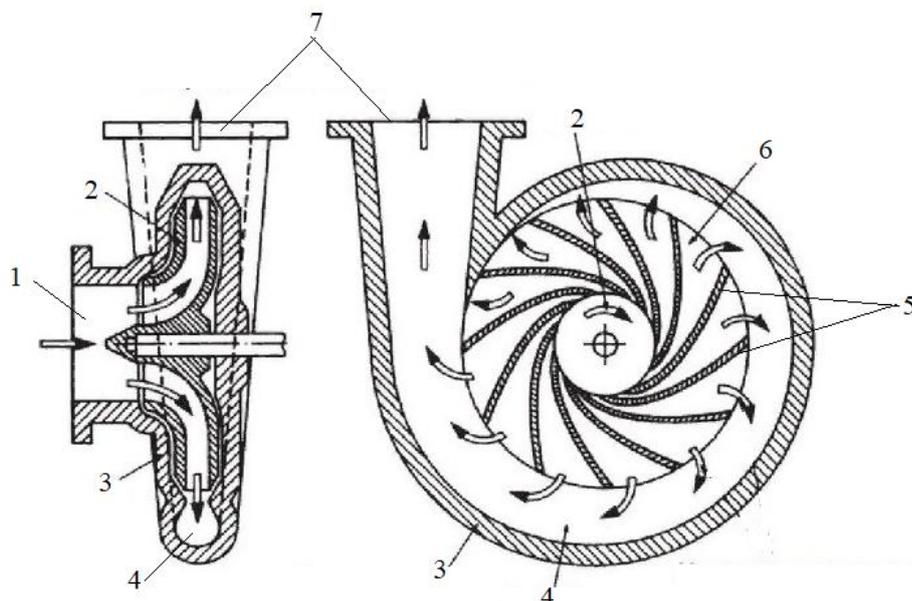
Схема устройства центробежного насоса: 1 – всасывающий патрубок; 2 – рабочее колесо; 3 – корпус насоса; 4 – объемная камера (диффузор), размещенный в корпусе насоса; 5 – лопасти; 6 – межлопастные каналы; 7 – напорный патрубок.
